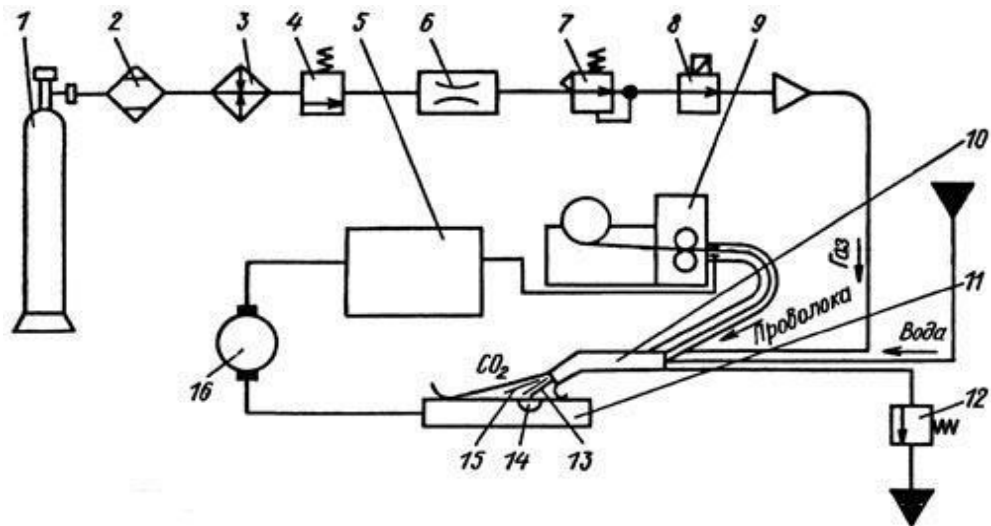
Схема установки для напівавтоматичного наплавлення в середовищі захисного газу: 1 – балон із газом CO_2 ; 3 – підігрівач; 2 – осушувач; 4 – редуктор; 6 – витратомір; 5 – шухляда апаратна; 8 – клапан електромагнітний; 7 – регулятор тиску; 9 – механізм подавання дроту; 10 – голівка; 12 – насос водяний із регулятором тиску; 11 – деталь, яку відновлюють; 13 – електрод; 14 – зварювальна ванна; 15 – шар газу (CO_2); 16 – джерело зварювального струму (генератор зварювальний) [1, 2, 3, 6, 8, 9].
